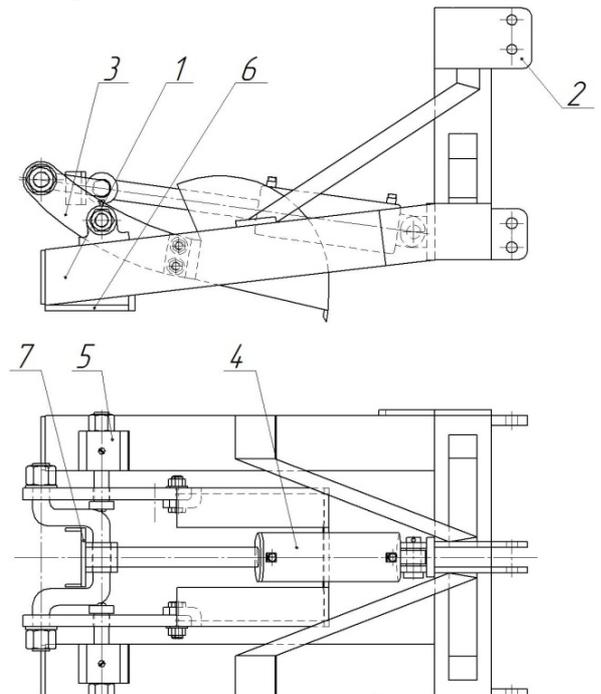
Конструкция машины для выкопки посадочного материала с комом почвы: 1 – рама с несущими брусьями; 2 – механизм навески; 3 – вертикальные стойки; 4 – гидроцилиндр; 5 – шарниры крепления вертикальных стоек; 6 – опоры; 7 – ограничитель (собственные разработки авторов)
